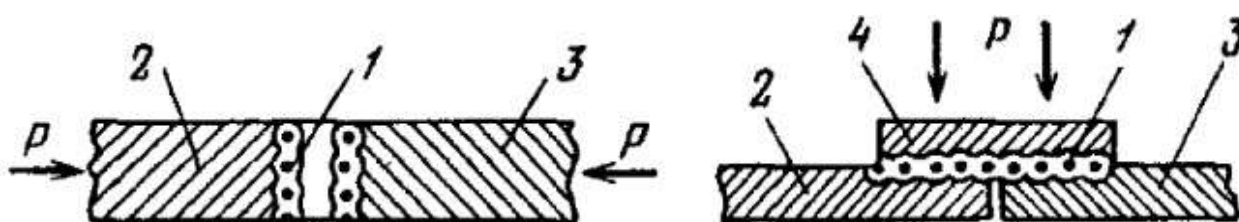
Схема зварювання нагрітим елементом, що залишається у деталі: 1 – нагрівальна спіраль, що залишається у зварному шві; 2, 3 - деталі, що зварюються; 4 – накладка
